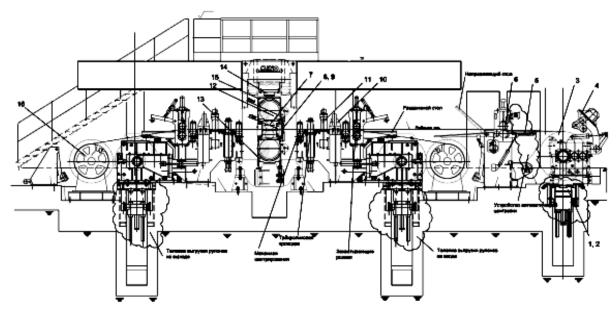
Одноклетьевой четырехвалковый реверсивный стан холодной прокатки 260/560x550 фирмы «MINO»
